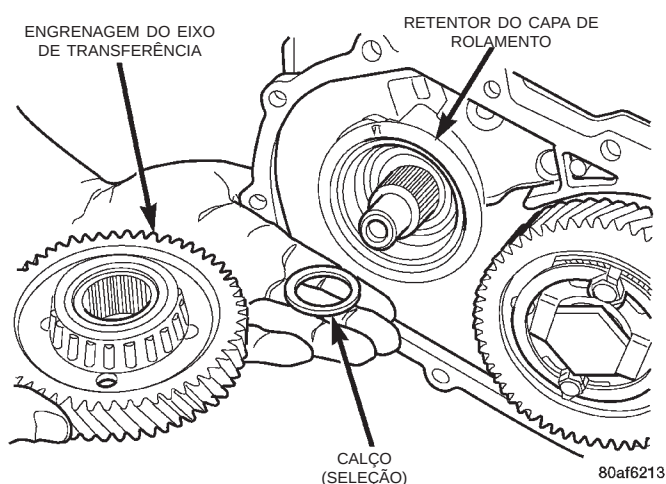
Engrenagem do Eixo de Transferência e Calço (Seleção)
